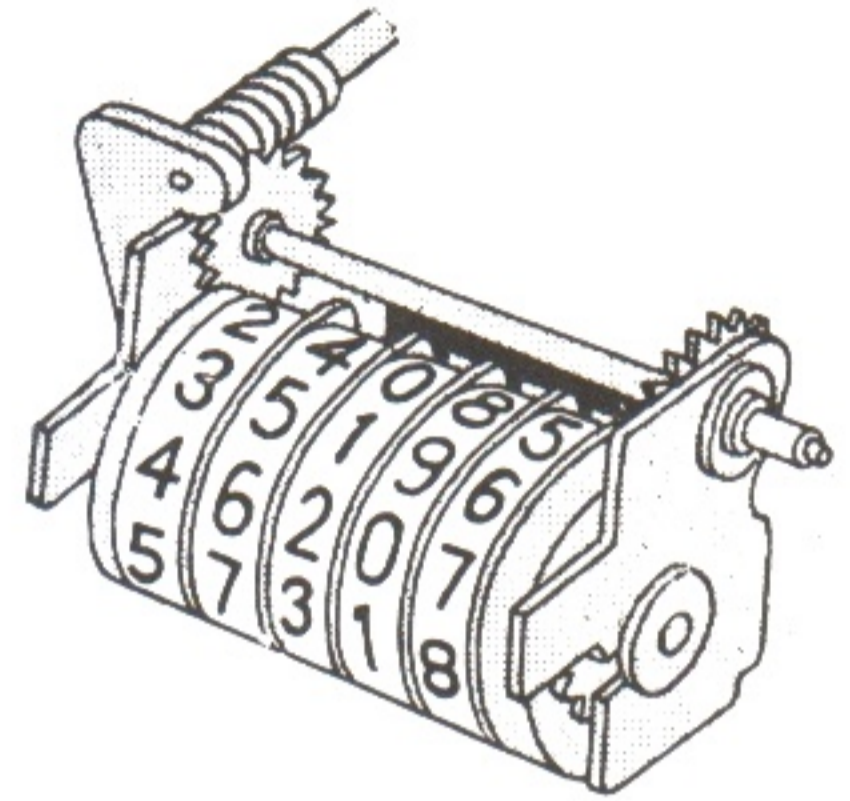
Tambor del contador kilométrico que constituye la base del cuentakilómetros.
